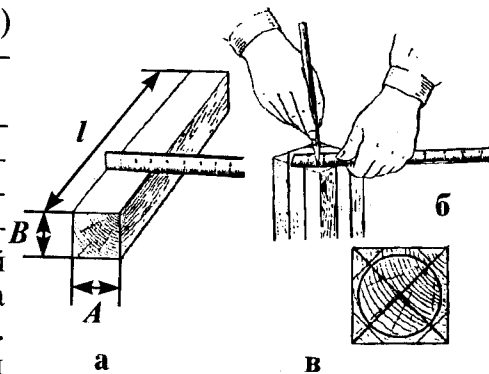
Подготовка заготовки для точения: а — измерение; б — разметка окружности, касательных и ребер восьмигранника; в — размеченный торец
